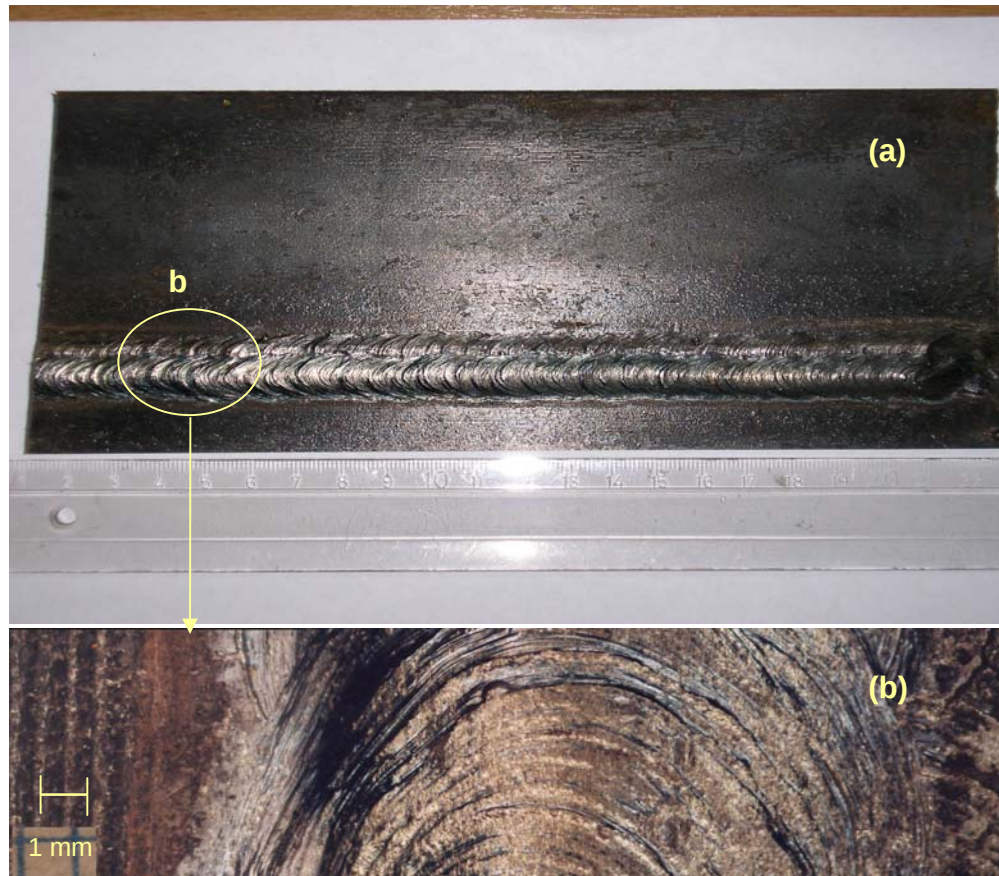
Cordón de Soldadura; (a) Vista General; (b) detalle de los rizos
